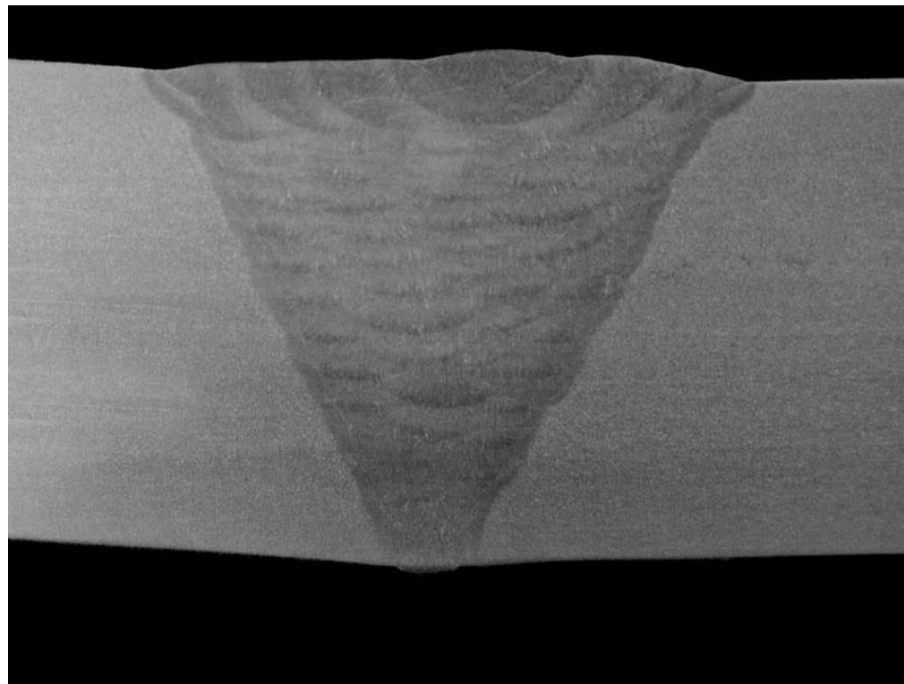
Ejemplo de una macrografía de una soldadura a tope
